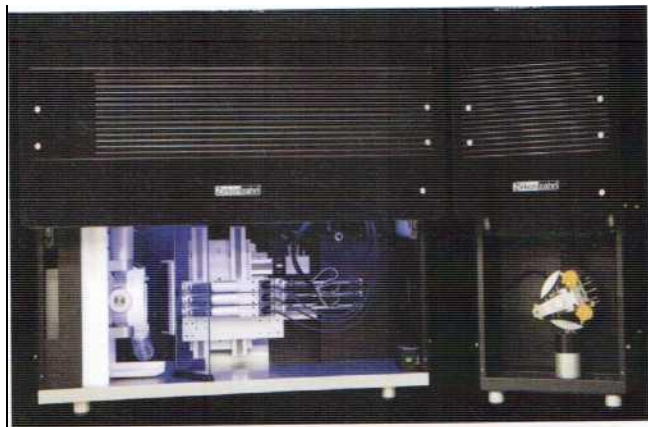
Отфрезеровано при помощи CAD/CAM System 5-TEC.
